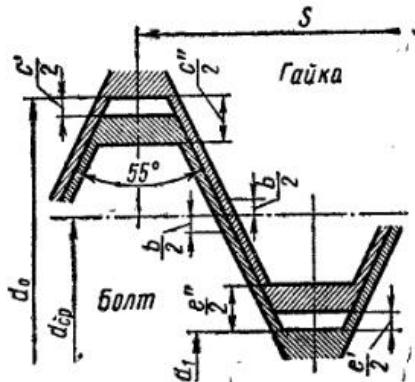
Схема расположения полей допусков для дюймовой резьбы:
